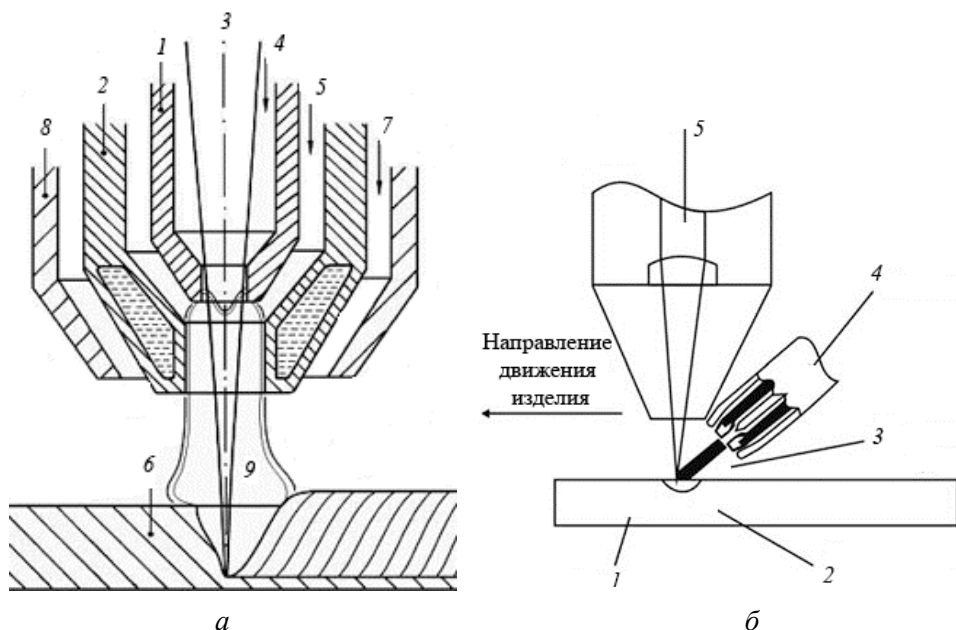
Схемы процессов сварки [4, 7]:
